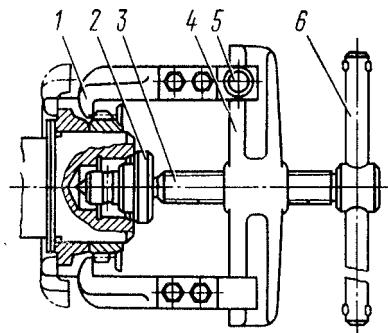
Снятие шестерни и заднего противовеса коленчатого вала съемником И801.01.000: 1 - захват; 2 - наконечник; 3 - винт; 4 - траверса; 5 - стопор; 6 - рукоятка
